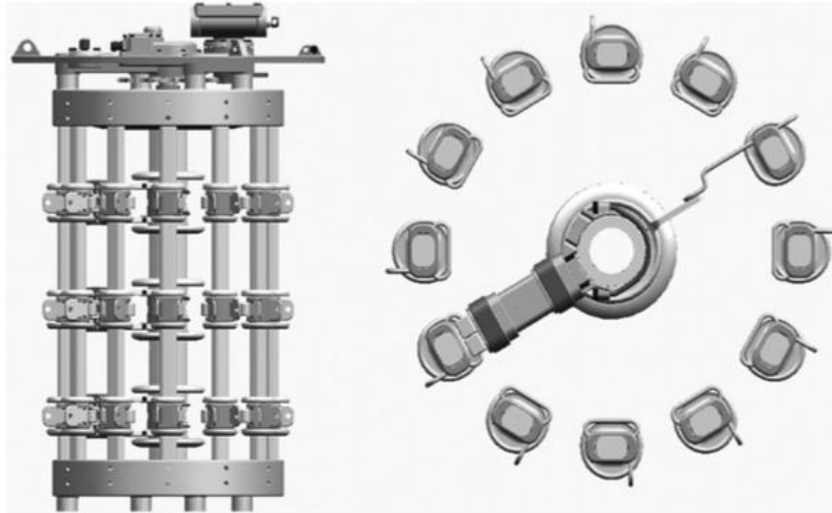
Alzado y planta de un DETC de operación mecánica rotatoria
